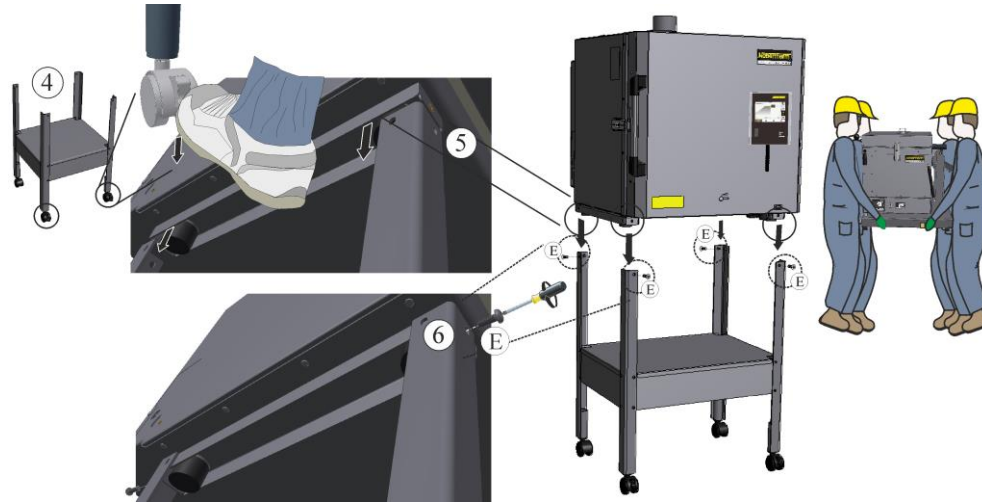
Taşıma makaralarının montajı (eğer mevcutsa)
